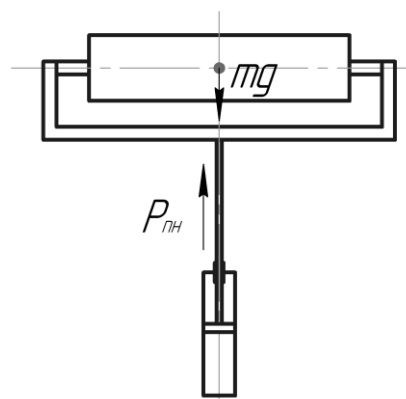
Розрахункова схема для підбору пневмоциліндра упору
